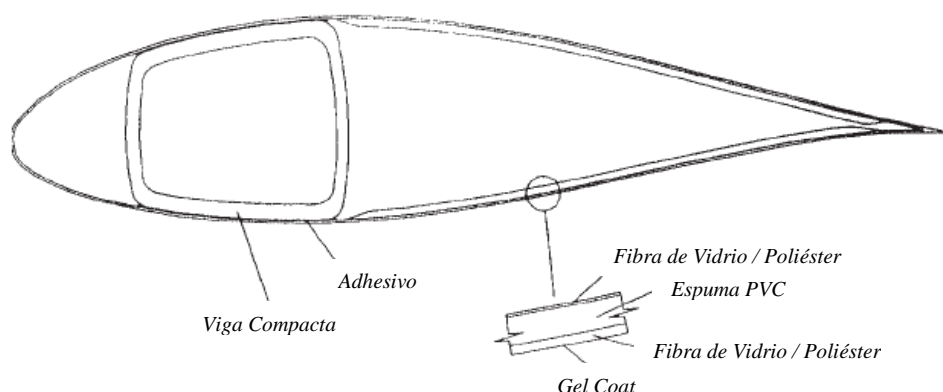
Estructura de concha con viga compacta de fibra de vidrio.
